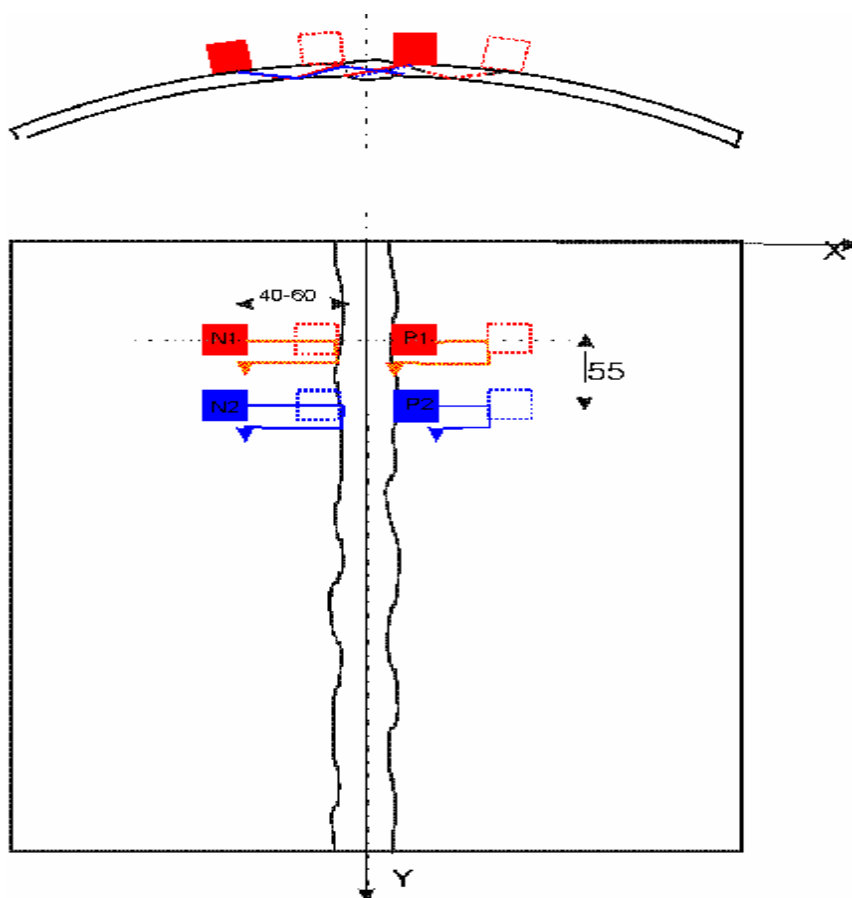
Схема контроля сварных образцов Выксунского металлургического завода.
